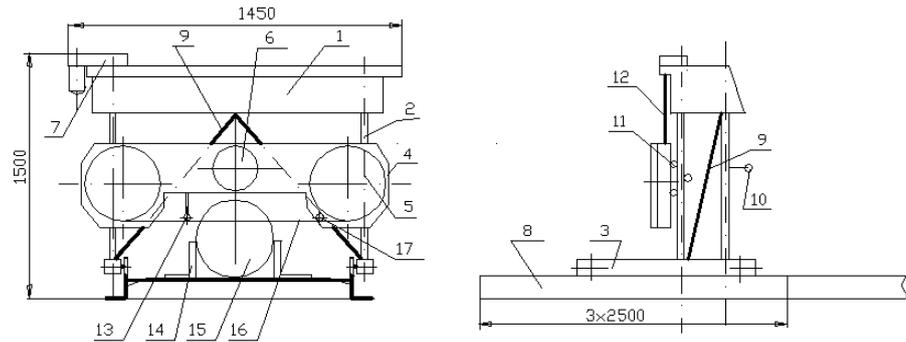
Схема ленточной пилорамы: 1 – балка портала; 2 – стойки; 3 – балка опорная; 4 – рамка пильная; 5 – колесо; 6 – главный двигатель; 7 – редуктор подъема рамки; 8 – секция направляющих; 9 – раскосы; 10 – поперечина; 11 – узел перемещения рамки; 12 – винт подъема; 13, 17 – подвижный и неподвижный упорные ролики; 14 – зажимные устройства; 15 – заготовка; 16 – пила ленточная
